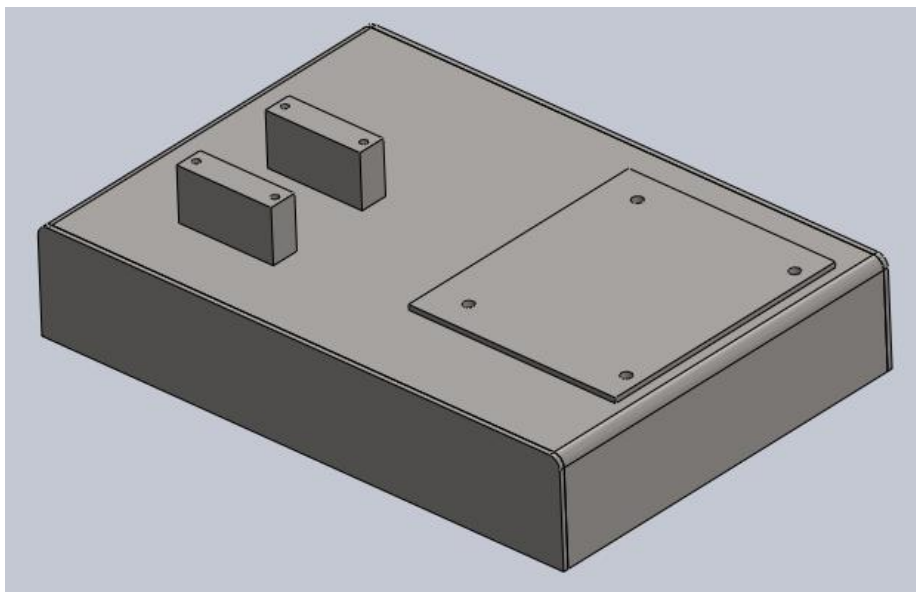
Caixaote da base. Chapas foram soldadas nas laterais
